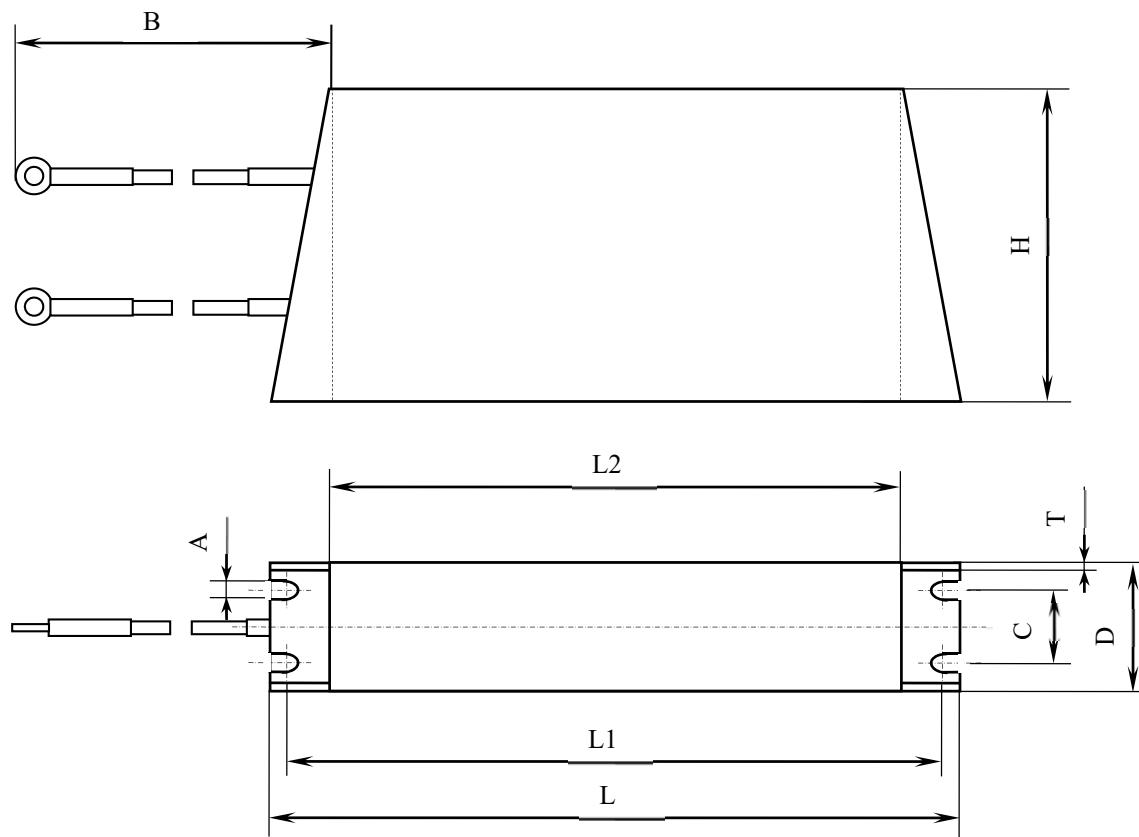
Габаритные и установочные размеры тормозного сопротивления RXLG
